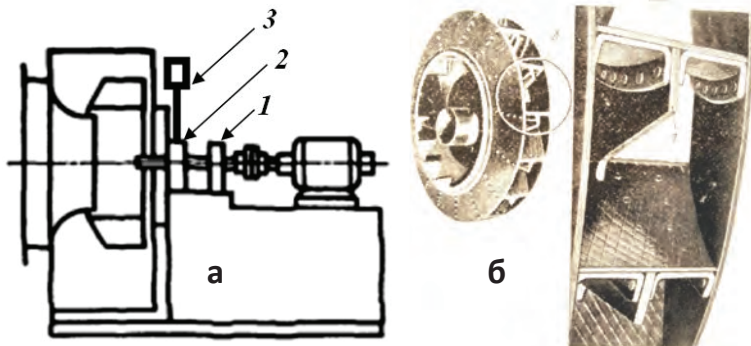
Дымосос: а) с демпфером (1 - радиальный подшипник; 2 - упорный роликовый подшипник; 3 - демпфер); б) рабочее колесо с "бронёй" (1 - диск с вырезами в виде звездочки) [1].
